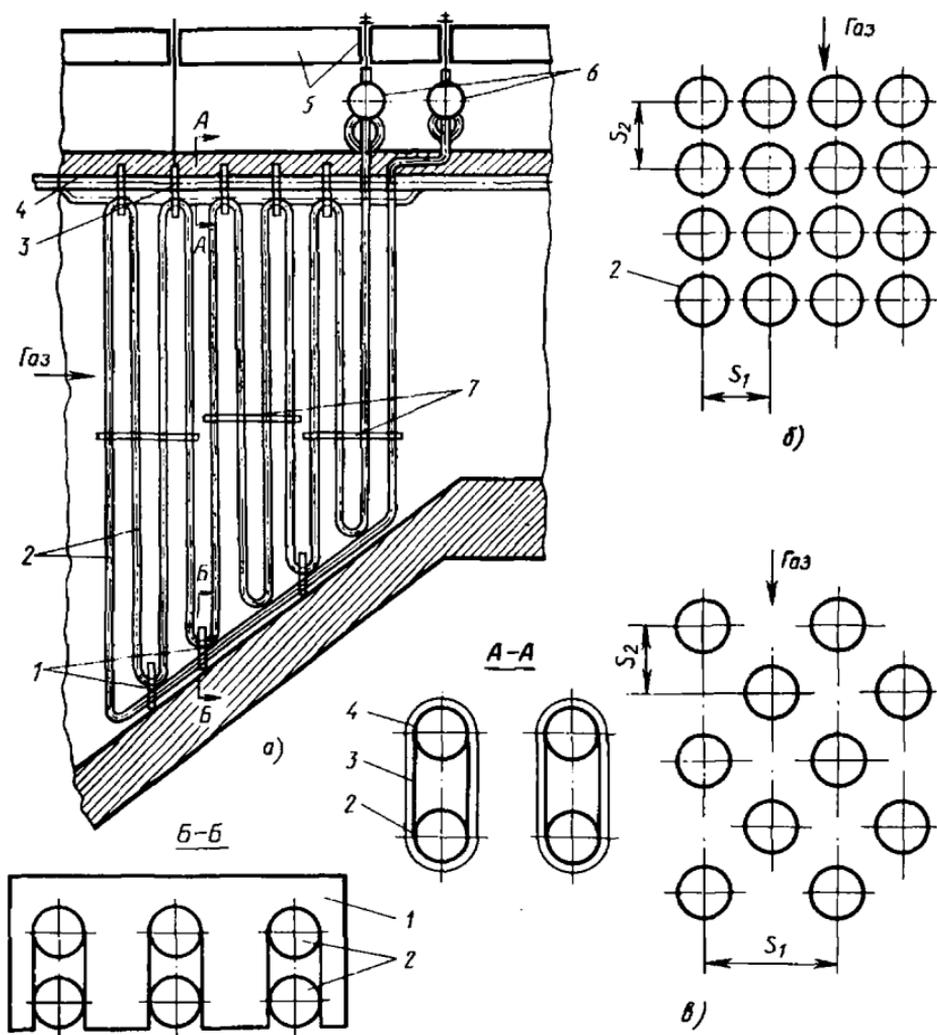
Пароперегреватель с вертикальными трубами (а) при их коридорном (б) и шахматном (в) расположении:
